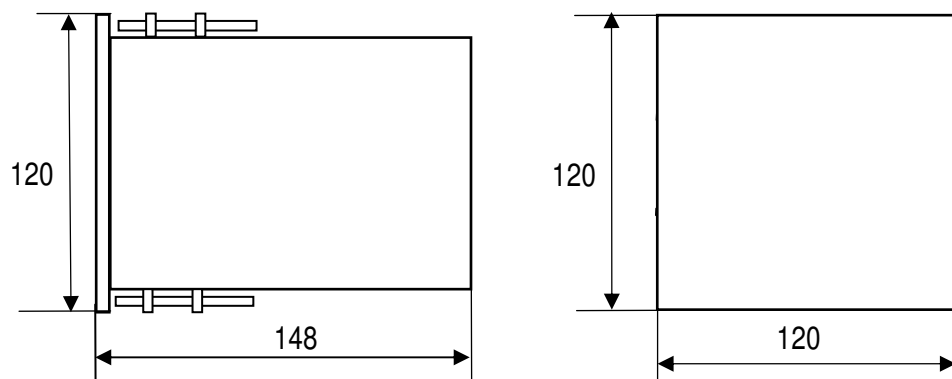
Габаритные размеры ЦП 9010У
